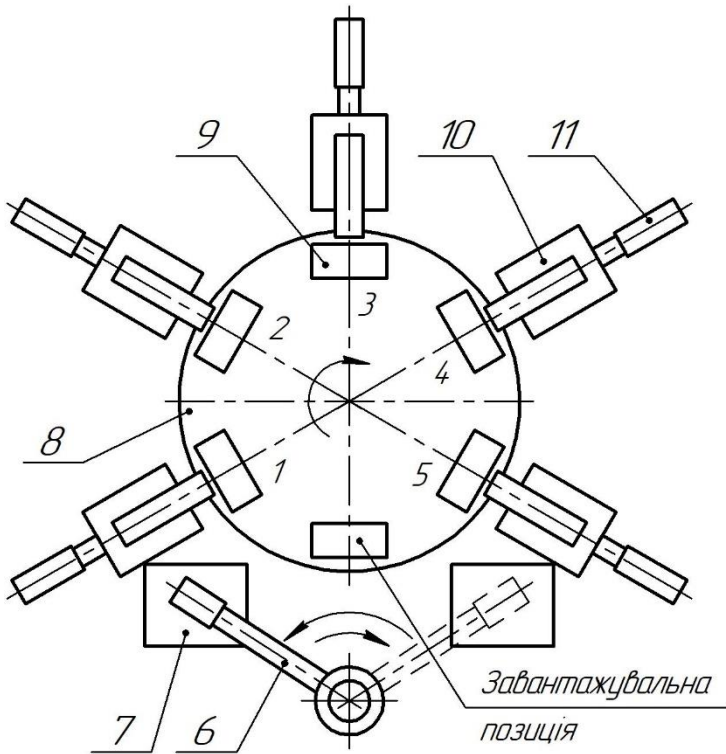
Схема компоновки складального багатопозиційного автомата: 1, 2, 3, 4, 5 – робочі позиції; 6 – маніпулятор; 7 – стіл; 8 – поворотний стіл; 9 – пристрій; 10 – складальна головка; 11 – магазинний пристрій
